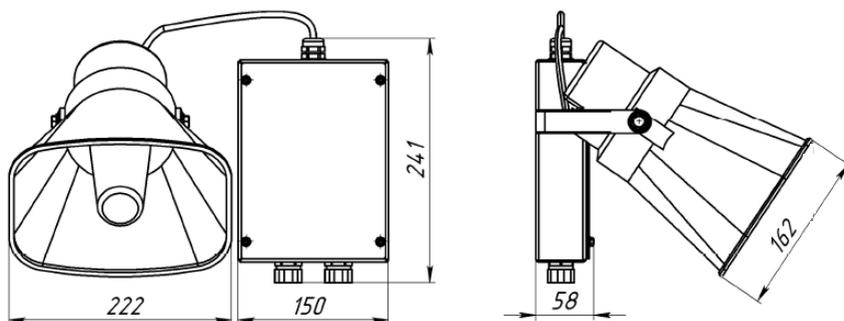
Габаритные и присоединительные размеры оповещателя
